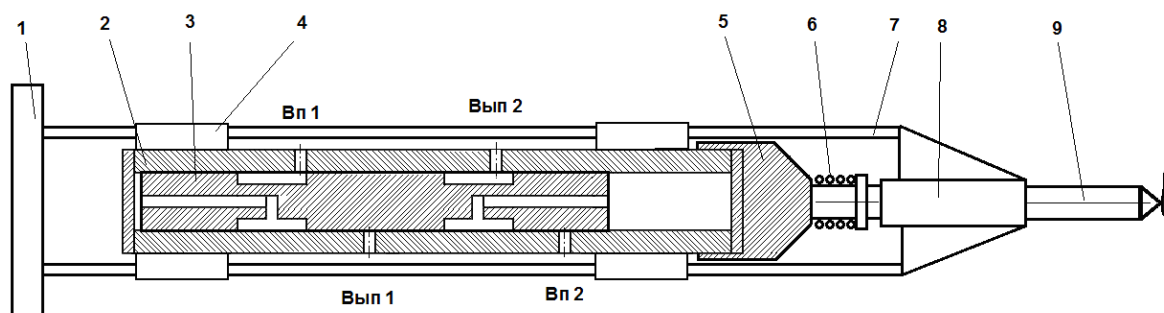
Схема пневматического молотка системы «корпус-ударник».
